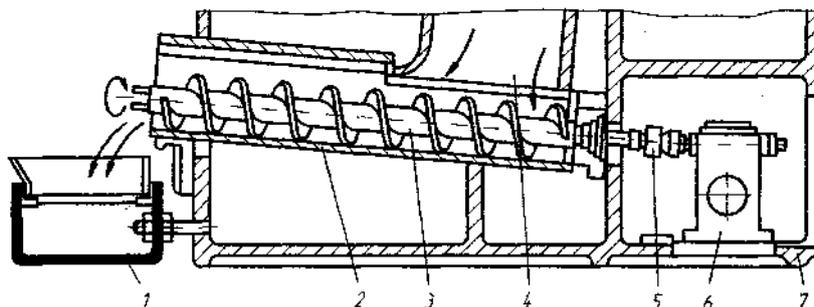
Шнековый конвейер для удаления стружки из станков
